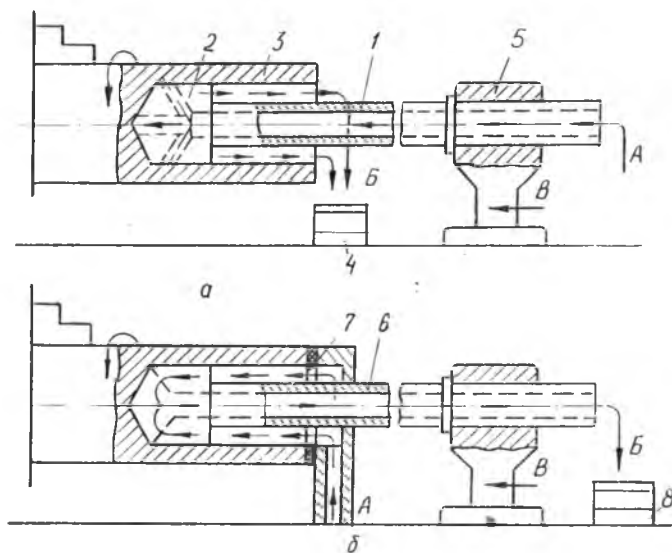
Схема подачи СОЖ при глубоком сверлении: а — с наружным отводом стружки; б — с внутренним отводом стружки
